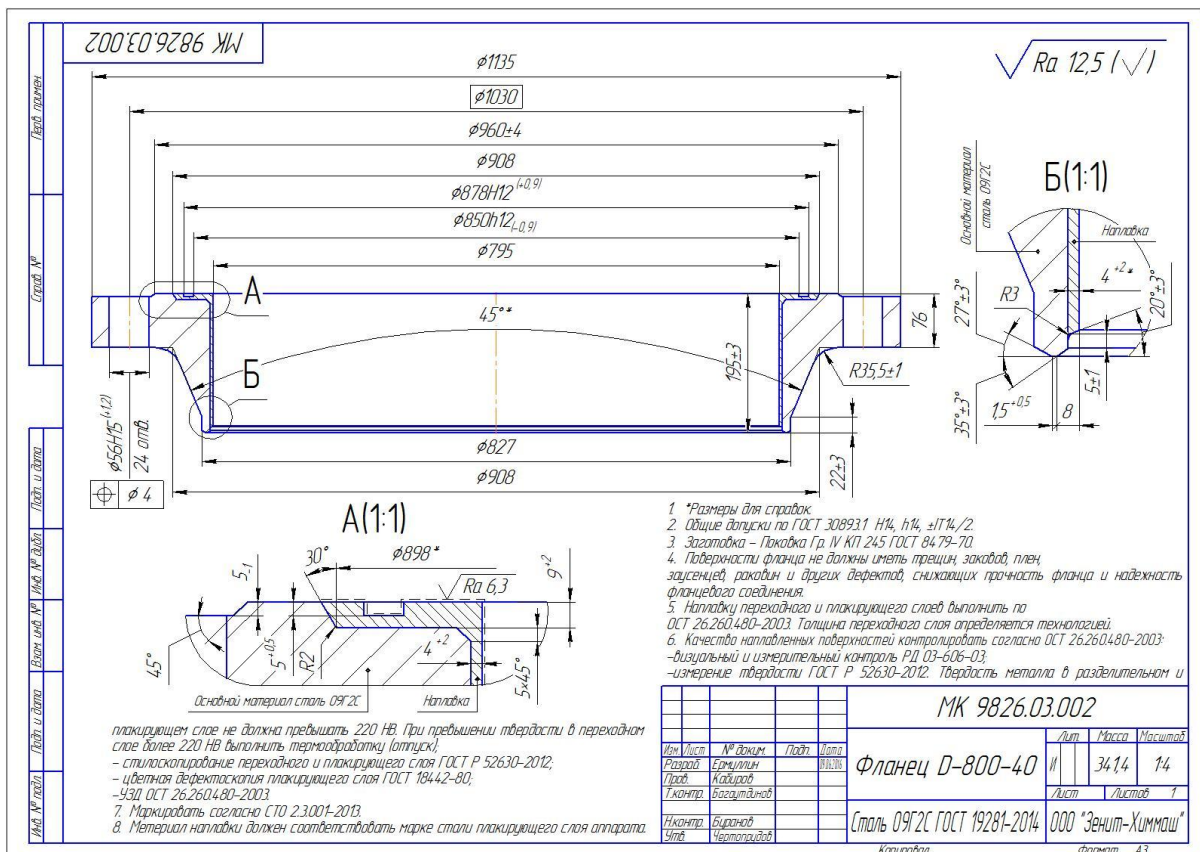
Чертёж фланца с наплавкой антикоррозионными материалами
